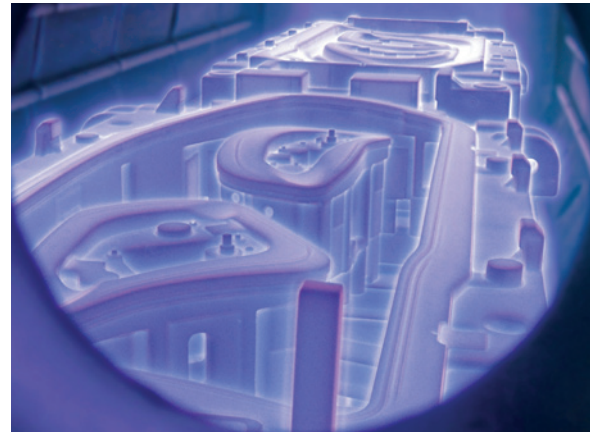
Oberflächenbehandlung von Umformwerkzeugen mittels BALITHERM® PPD
